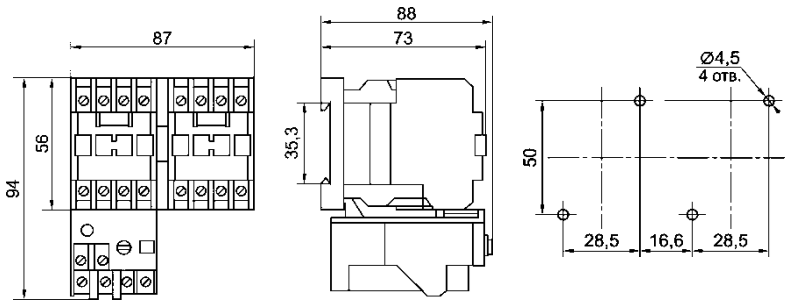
Пускатель реверсивный ПМ12-010 10А.
